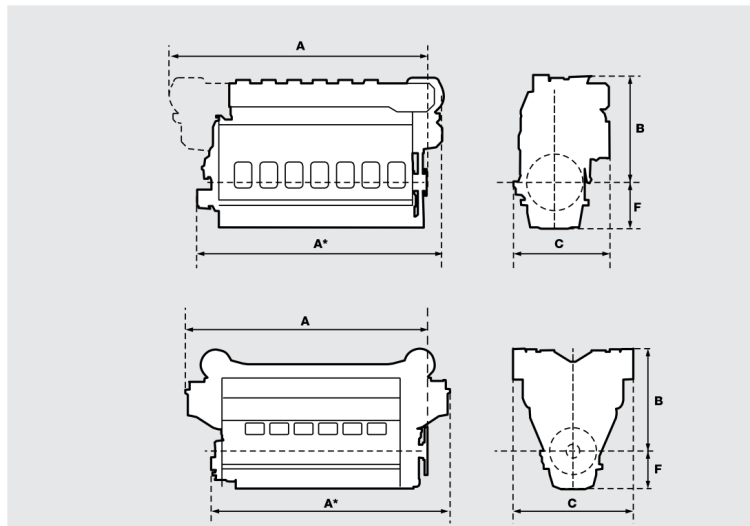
Dimensiones motor Wärtsilä 12V64
